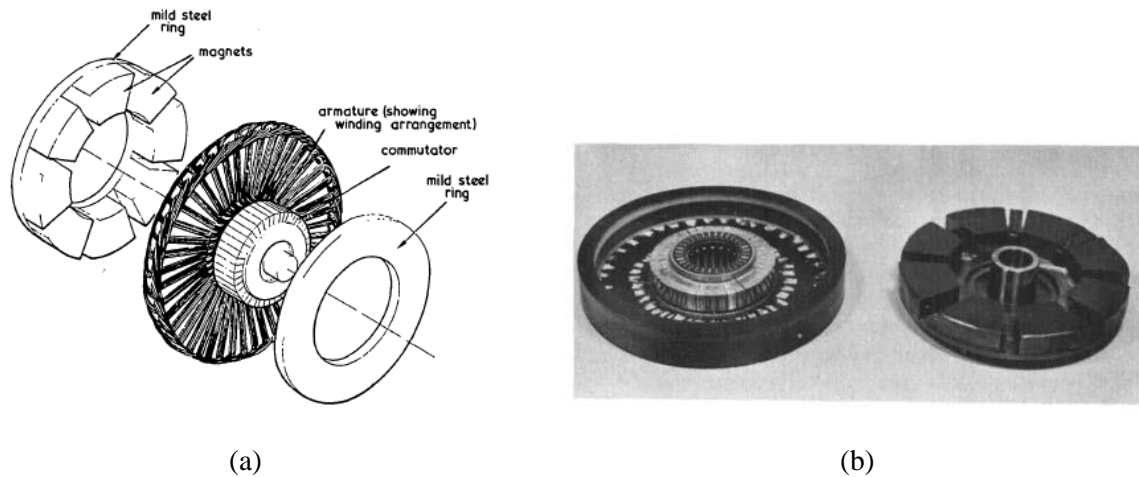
SPM à flux axial à un seul entrefer à stator sans encoches : (a) schéma de la machine éclatée et (b) prototype de la machine [30].
